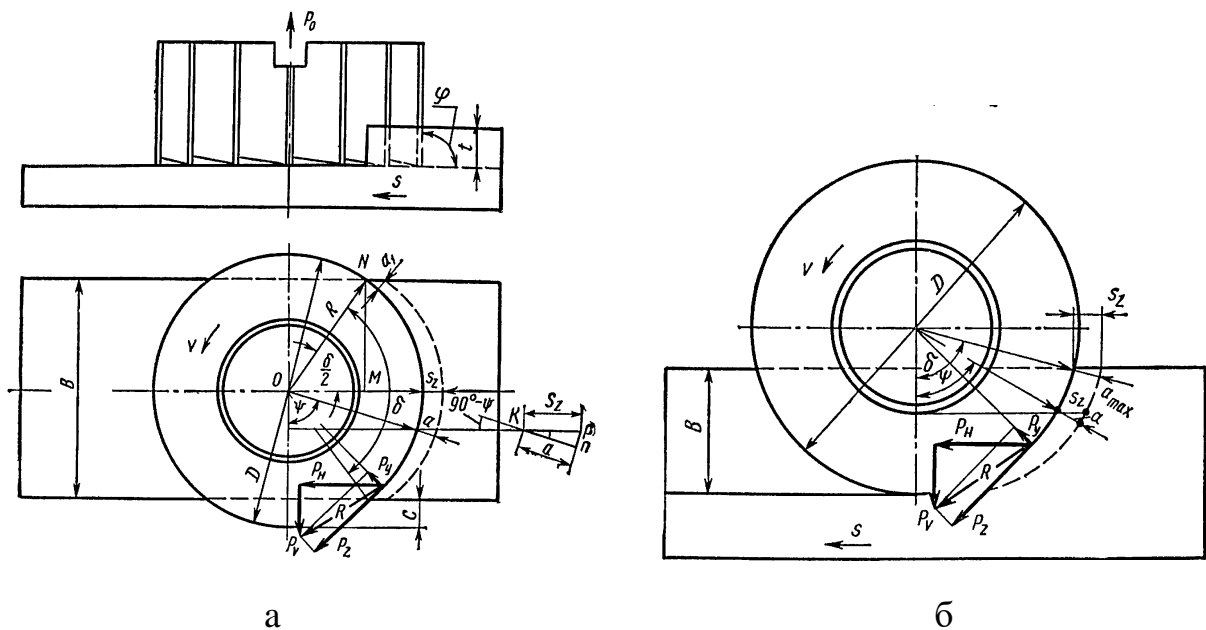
Торцеве фрезерування [2 с. 261]
